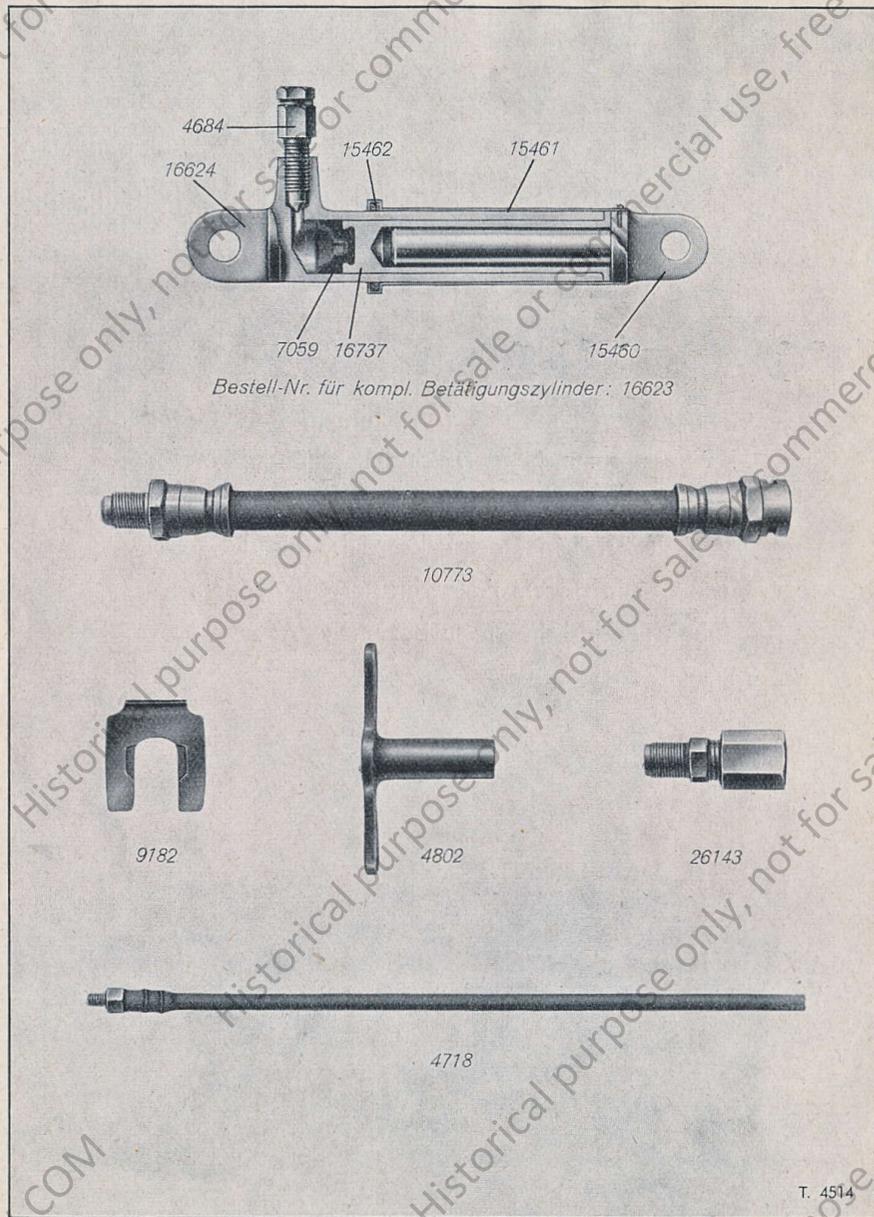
Bezeichnung der Einzelteile siehe Seite 42
